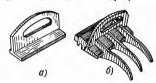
Проверка пальцевой секции шаблоном: a — кондуктор; 6 — проверка кондуктором.
